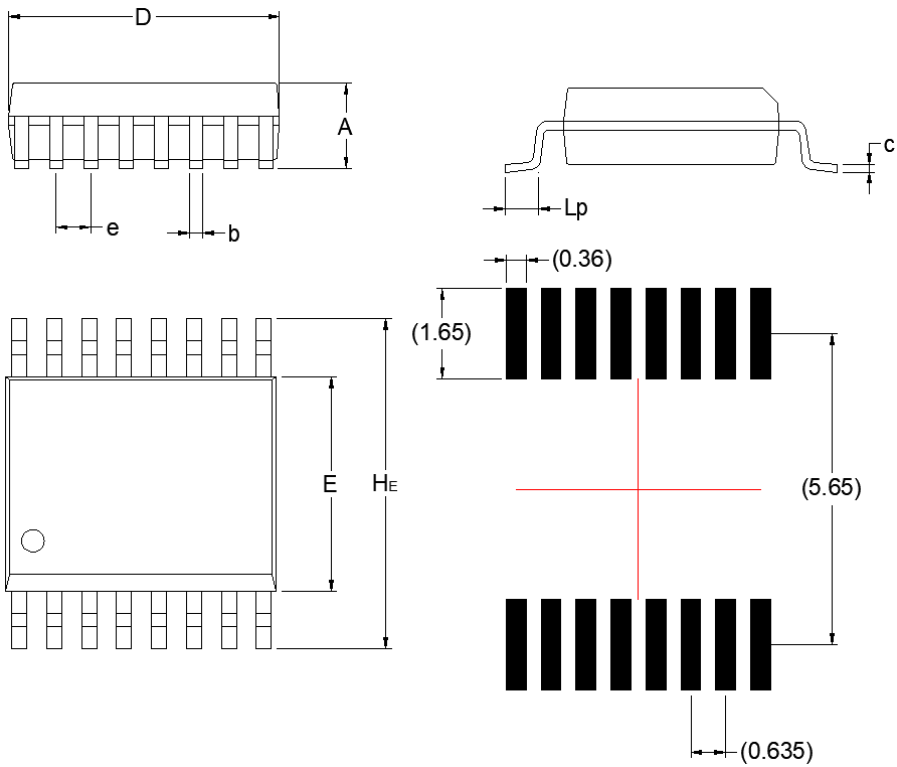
小间距 SSOP16 封装外形图 PCB 焊盘参考设计
